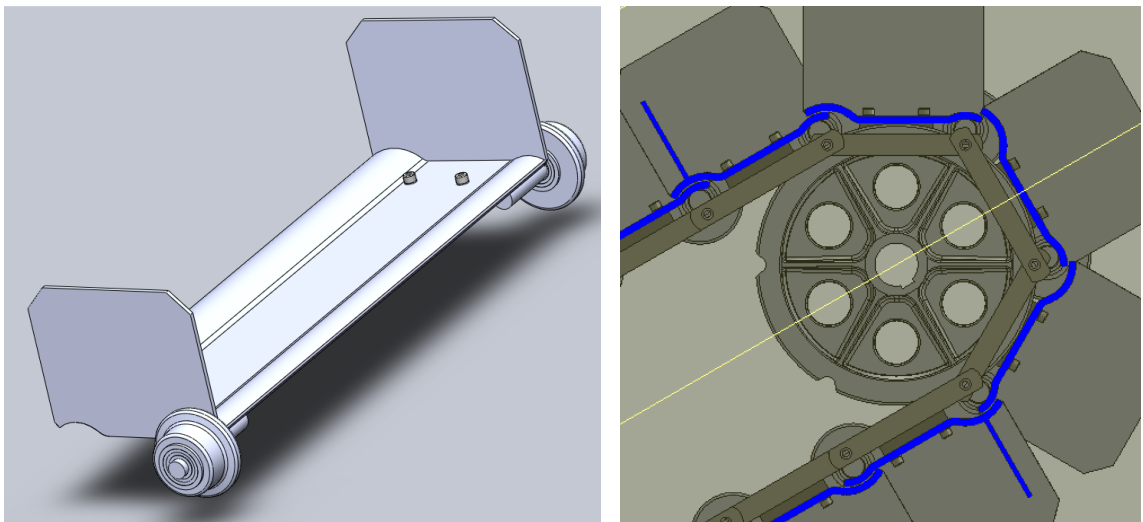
a obr. 7 – Řetězová kola pro dopravní řetěz MC 28
